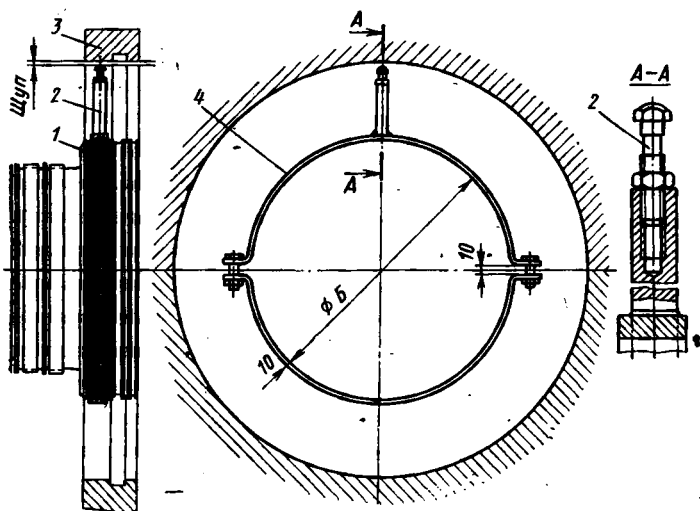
Схема приспособления для центровки роторов по точкам под уплотнения:
